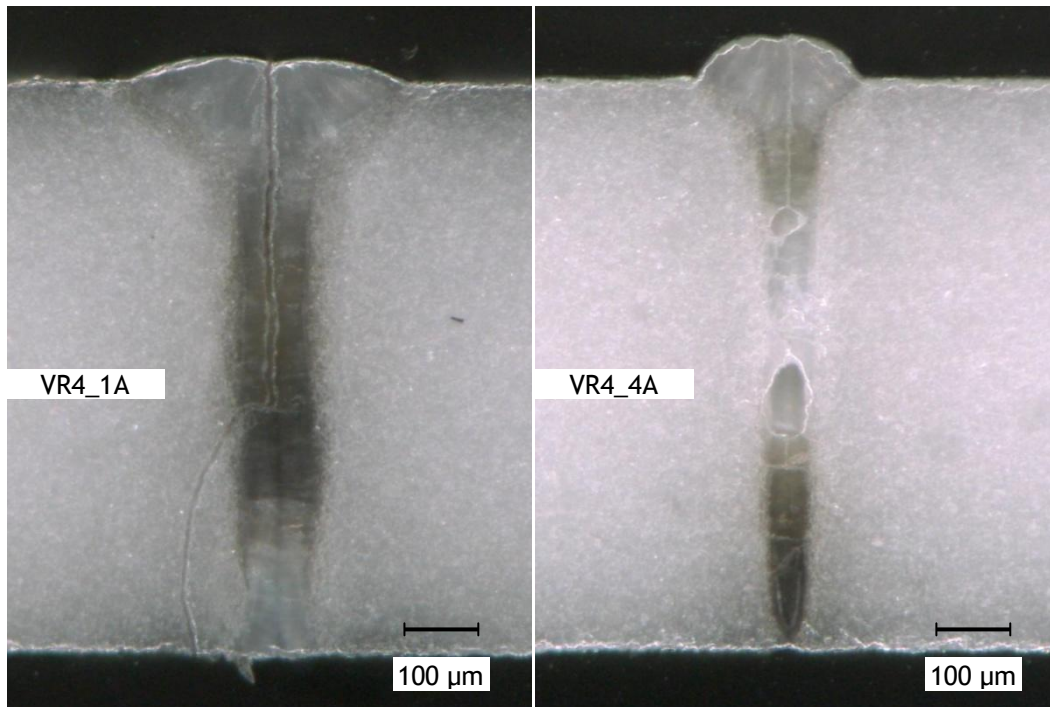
Beispiele für ungünstige Schweißnähte aus Versuchsreihe 4
